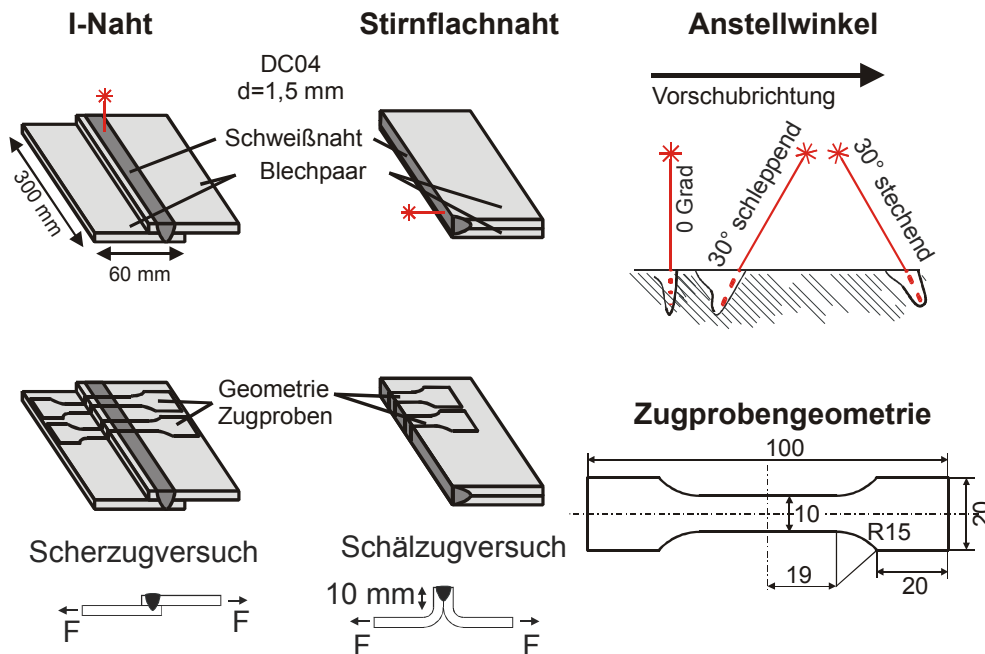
Geometrie der Probeschweißungen, Anstellwinkel und Zugprobengeometrie
